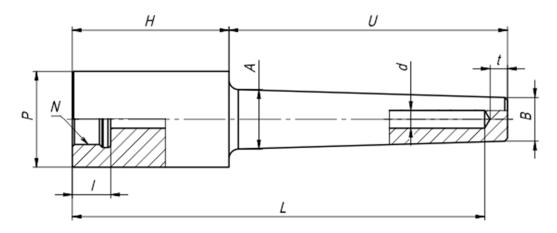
Гильза под приварку через адаптер (Socket Weld), цельноточёная, коническая, под неподвижный штуцер.
